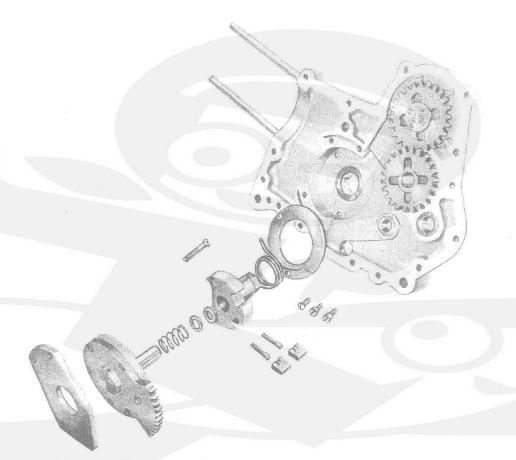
Gruppo preselettore, osservare l'ordine di montaggio
